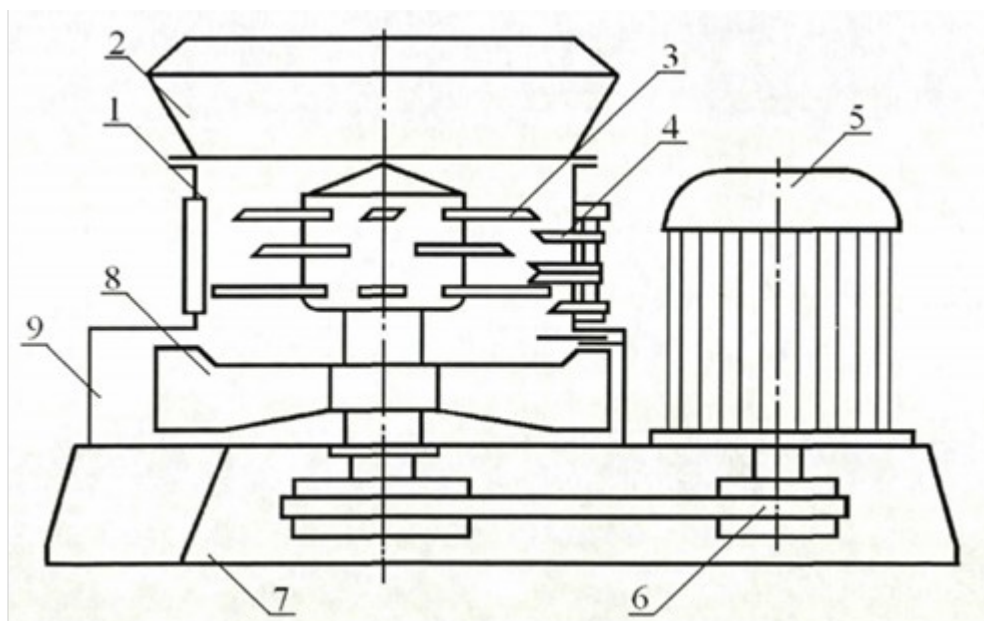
Кормоподрібнювач-змішувач ІСК-3: 1 – робочий об’єм; 2 – приймальна камера; 3 - лопаті несучого гвинта; 4 - ніж; 5 – електродвигун; 6 - клинопасова передача; 7 – рама; 8 - швирилка; 9 – вивантажувальне вікно
